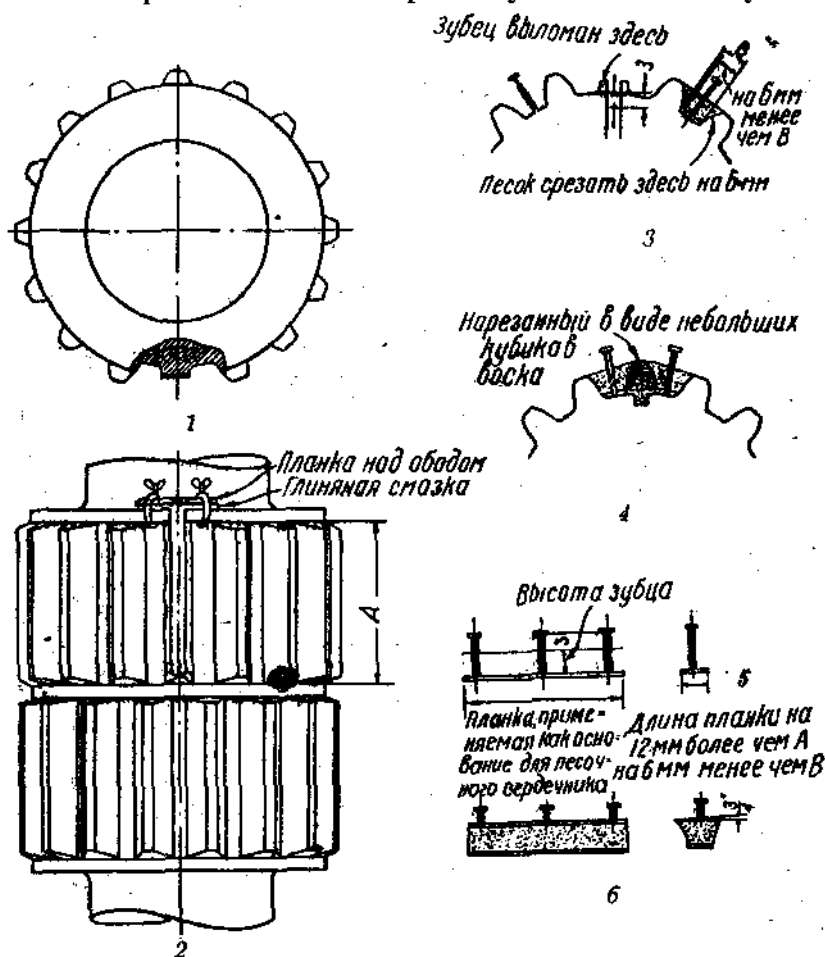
Последовательный ход подготовительных работ и сварке зубцов в шестеренном валке.
